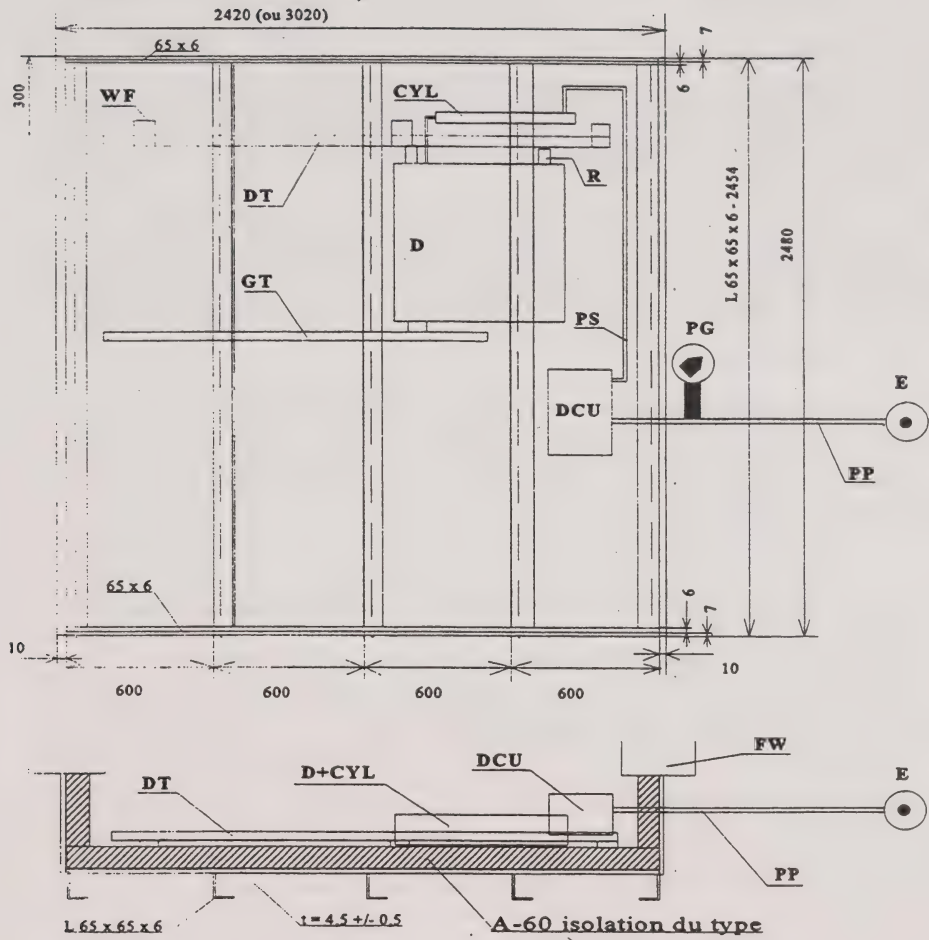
Arme destinée à recevoir le prototype de dispositif de commande des portes d'incendie.
